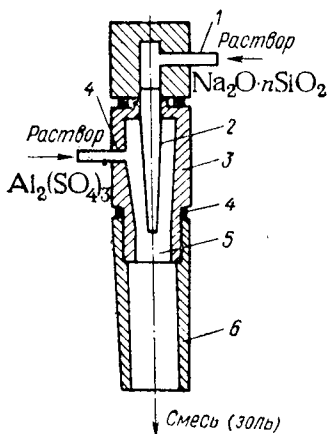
Металлический смеситель инжекторного типа: 1—нипель; 2—сопло; 3—корпус смесителя; 4—резиновая прокладка; 5—камера смешения; 6—успокоитель.
